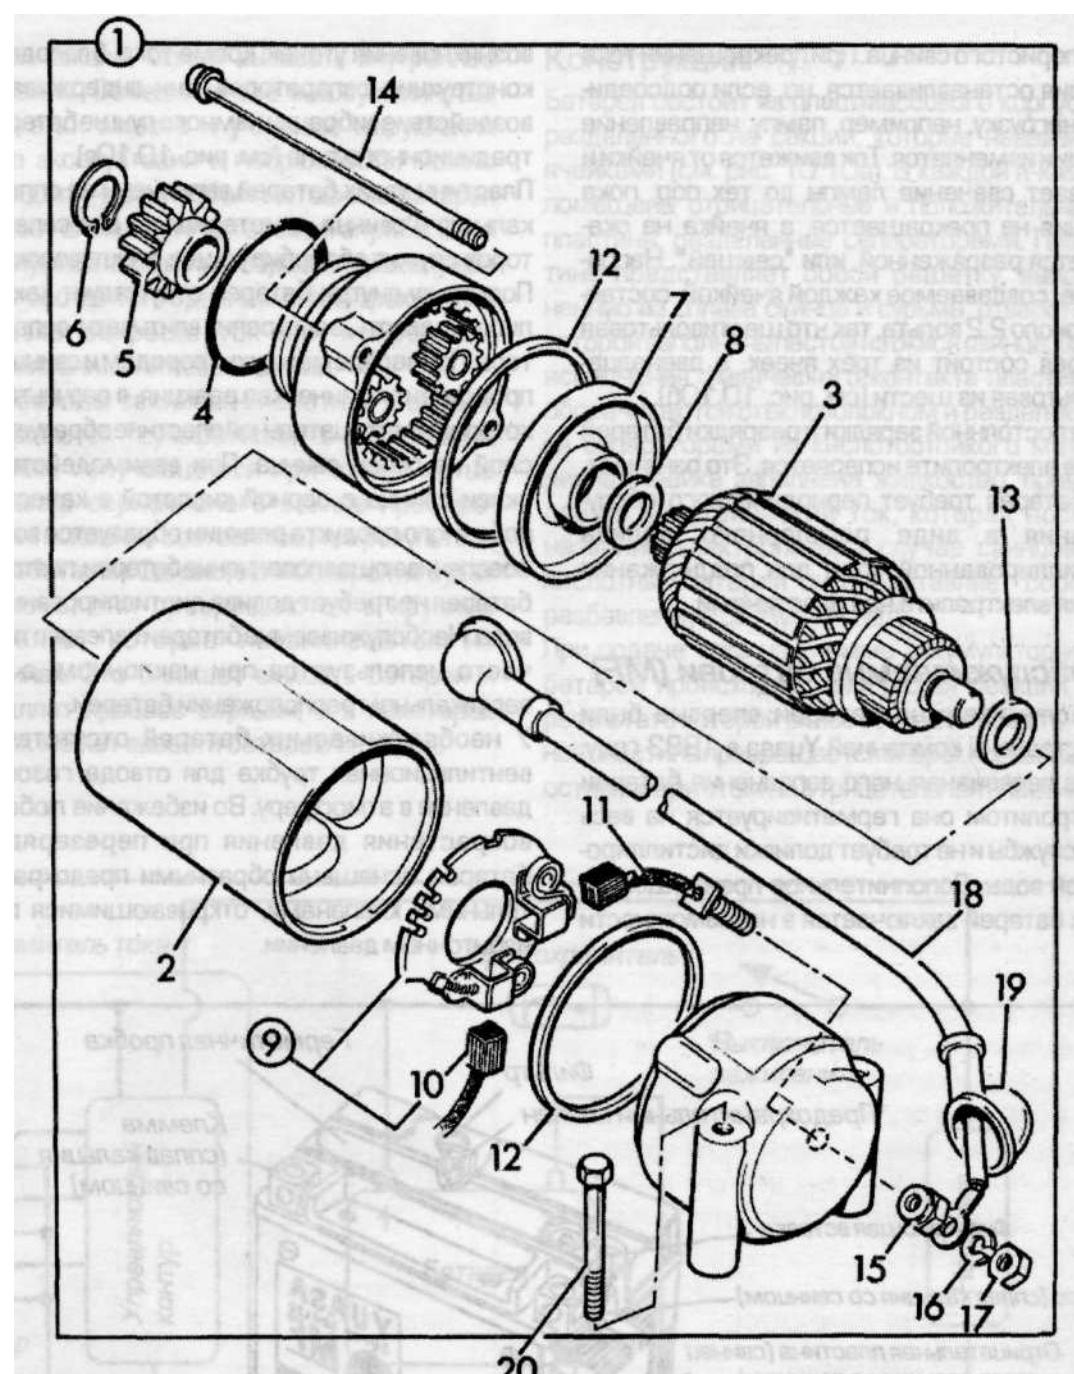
б Детали типичного электродвигателя стартера с двумя щетками
